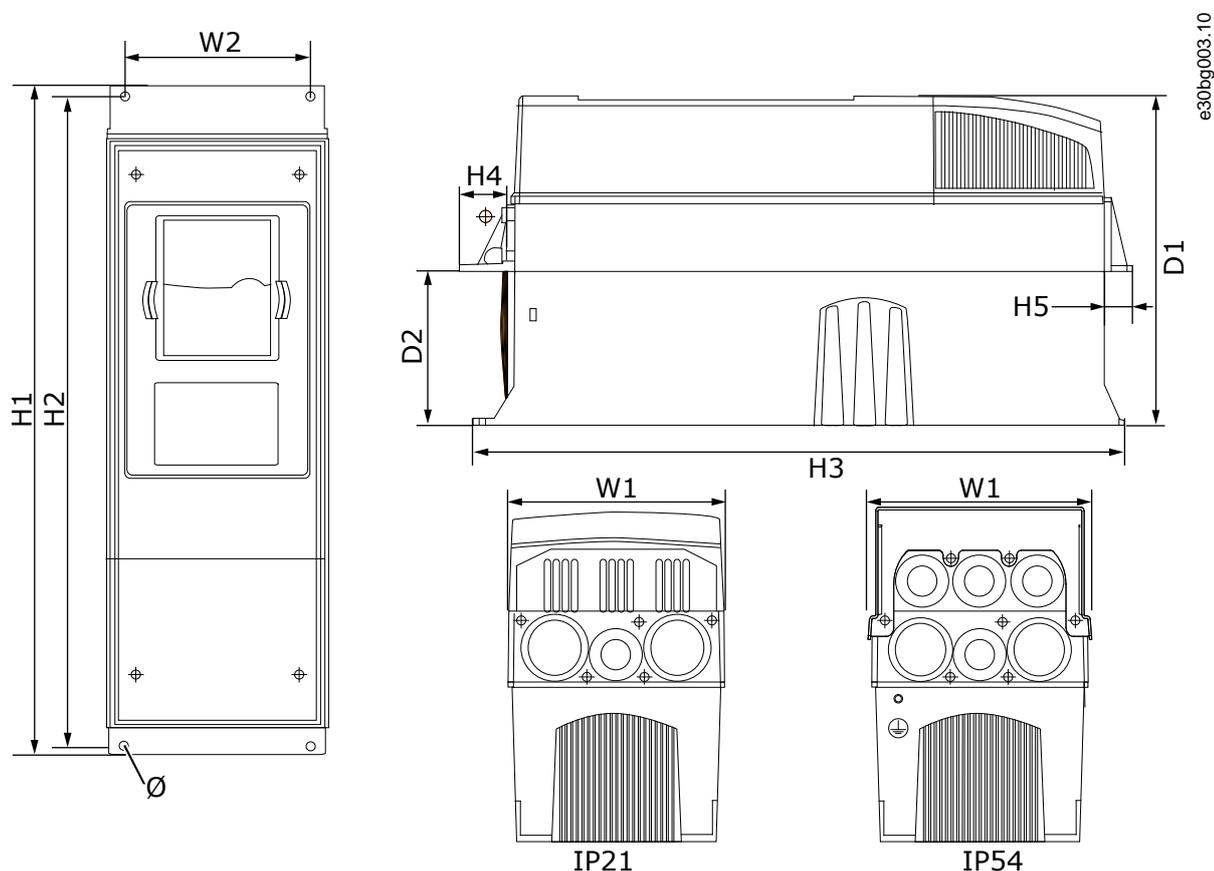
Dimensões do conversor de frequência com flange VACON® NXS/NXP, FR4-FR6
